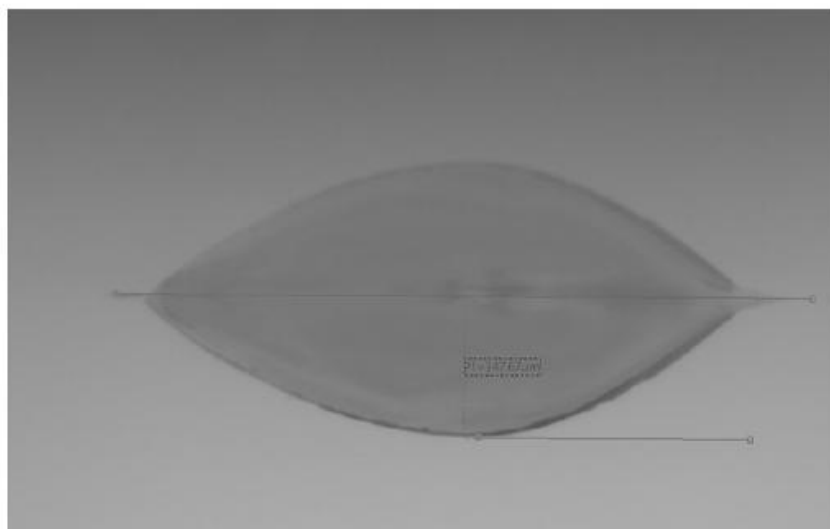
Сварное соединение двух пластин, вид сверху
